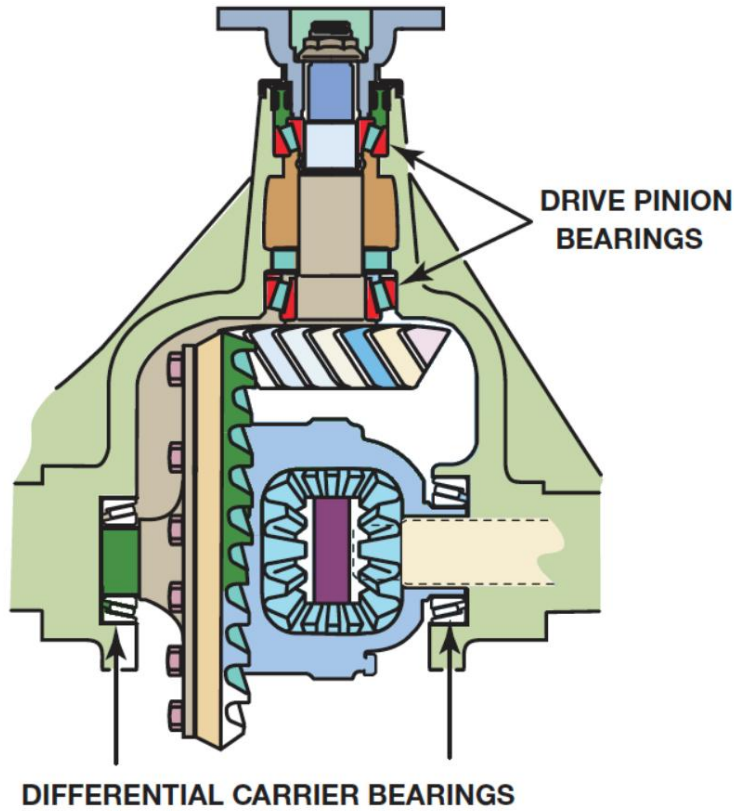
Engranaje anular, caja del diferencial y cojinetes del portador.
